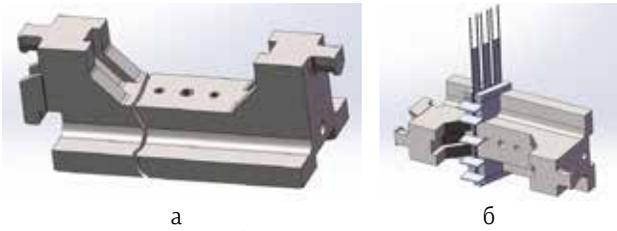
Ремонт корпуса бойка к прессу усилием 5000 тс с простой трещиной, расположенной в одной плоскости: а – схема развития трещины в корпусе бойка; б – схема электрошлаковой сварки корпуса бойка при его ремонте
